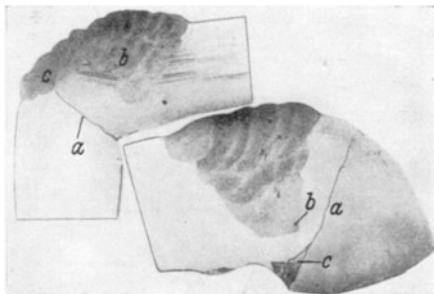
Elektrische Fehlschweißungen bei der Ausbesserung einer Wasserkammer ( $V = 1/2$ ).
